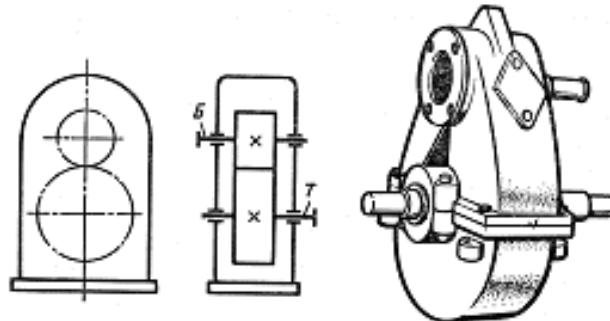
Одноступенчатый цилиндрический редукторы вертикальный
